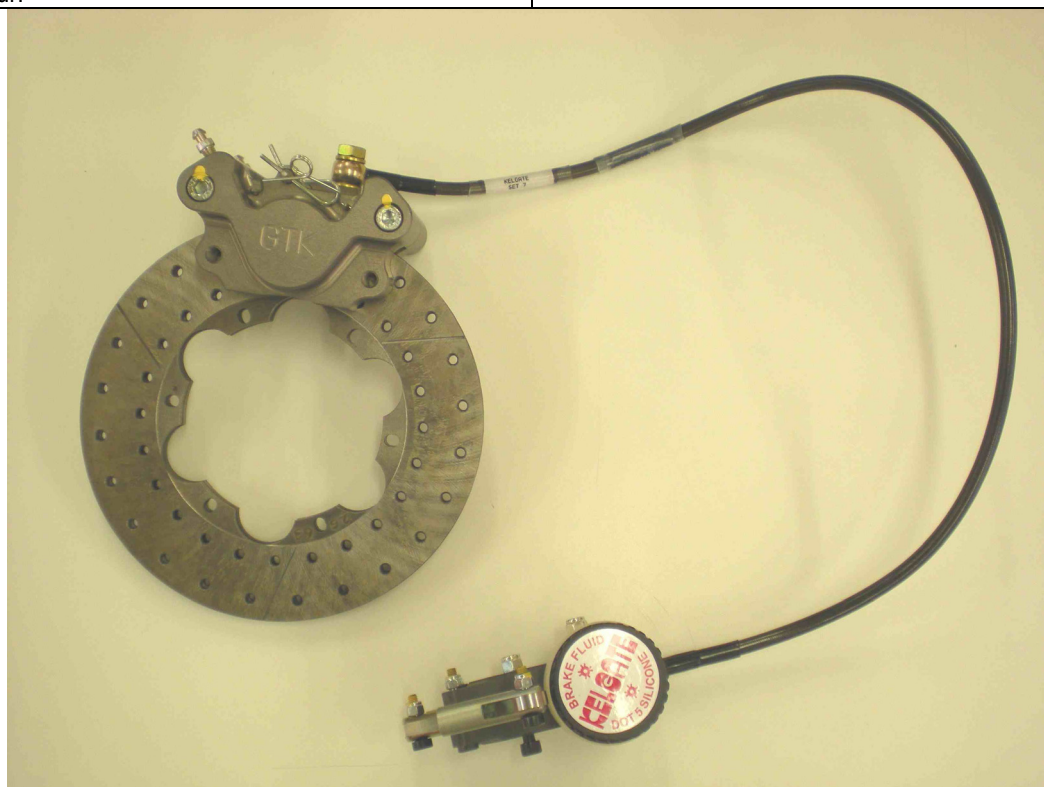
PHOTO VUE DE DESSUS DU SYSTÈME COMPLET ASSEMBLÉ
